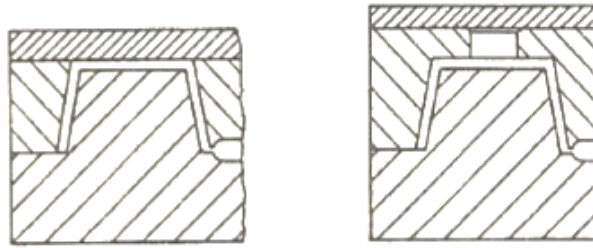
Molde con junta adicional, expulsión de aire por la junta adicional (izquierda), expulsión mediante troquel auxiliar (derecha).
